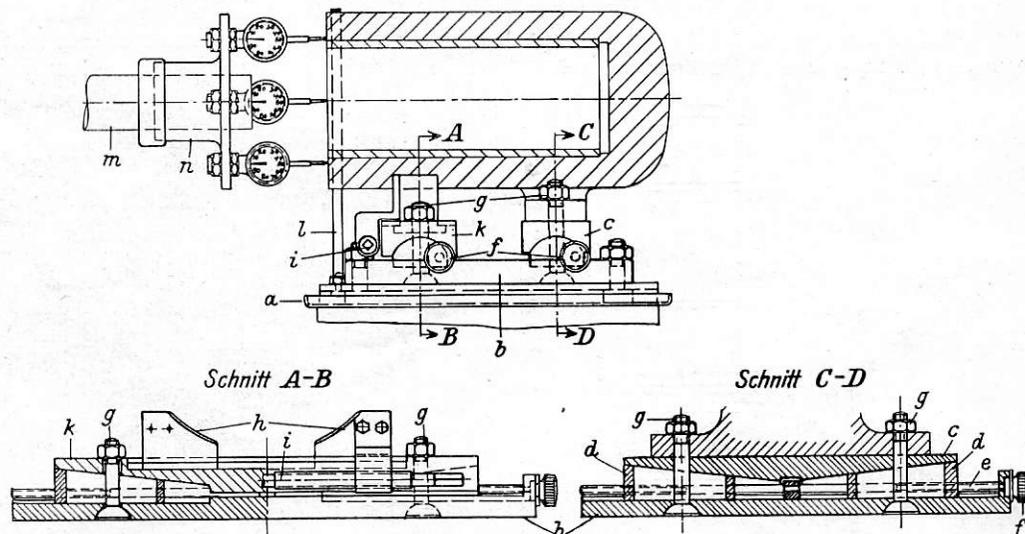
Vorrichtung zum Nachdrehen der Wasserzylinderbüchsen.
